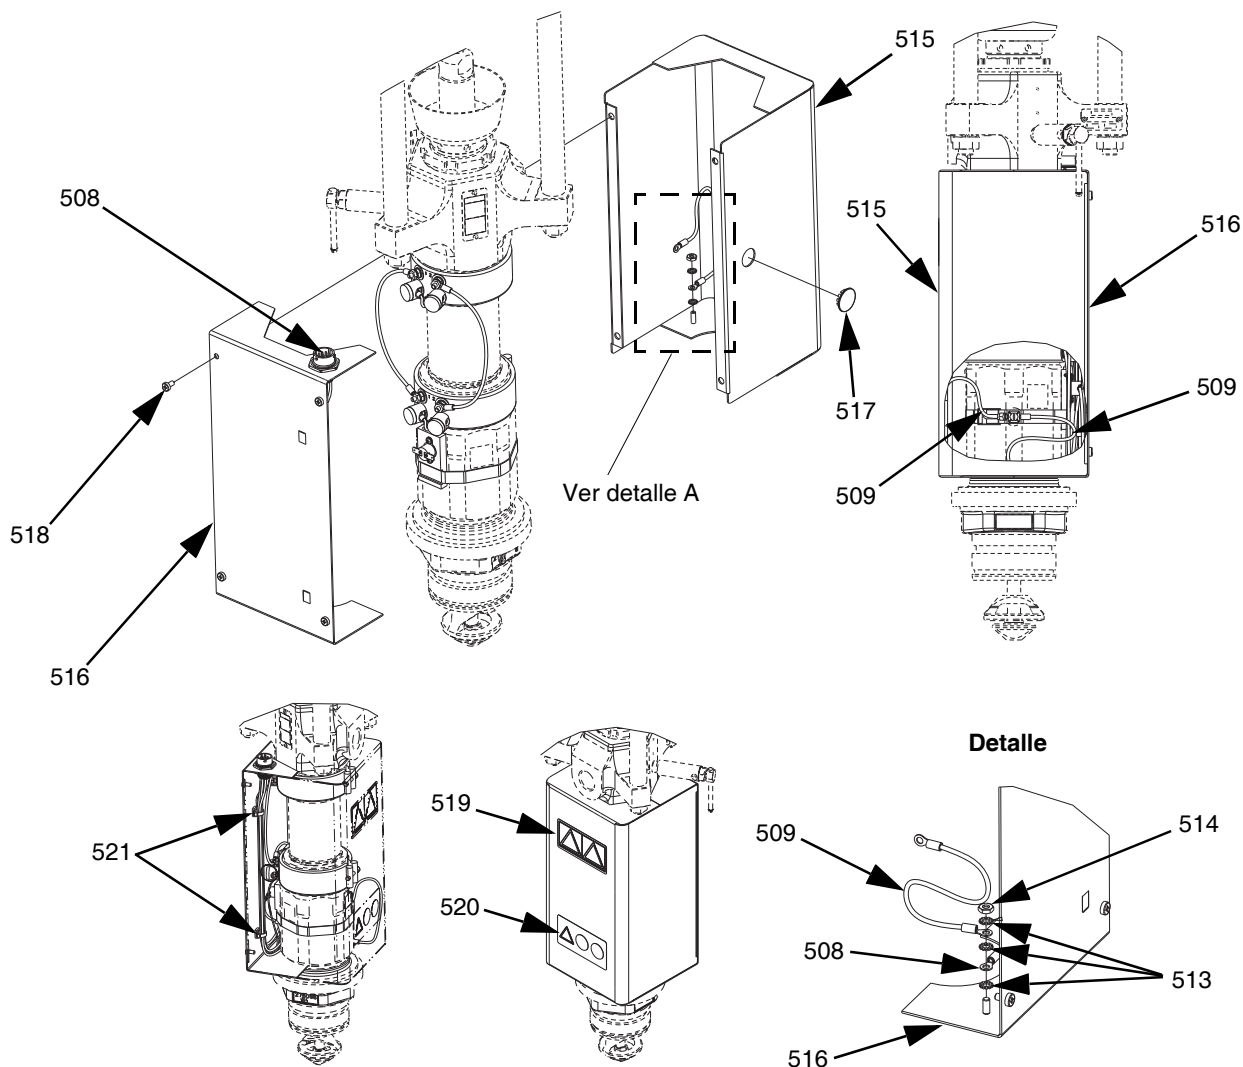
Kit de calentador de bomba Check-Mate 200 CS, 25R450
